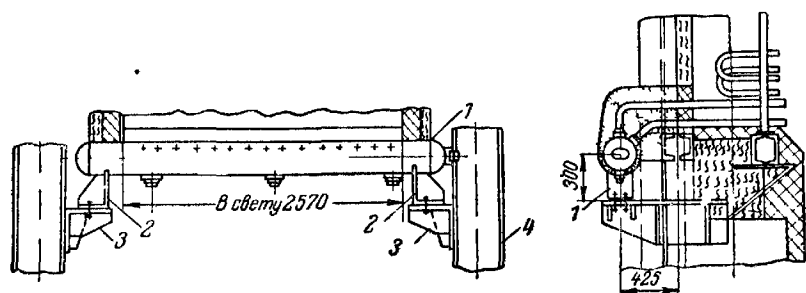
Крепление коллекторов конвективных поверхностей нагрева.
